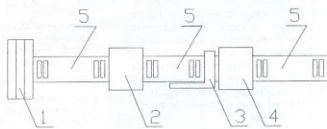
Схема расположения оборудования полуавтоматической линии: 1 — ножницы; 2, 4 — прессы; 3 — установка высокочастотная для нагрева; 5 — роляги
